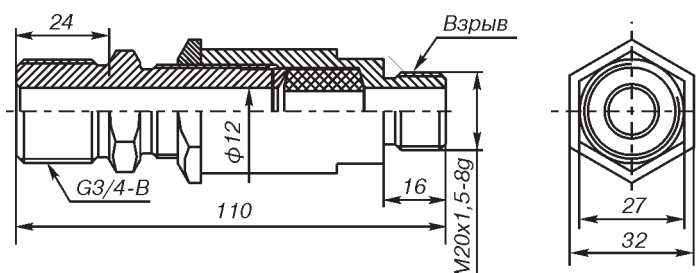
Кабельный ввод для трубного монтажа (ТБ 3/4").
